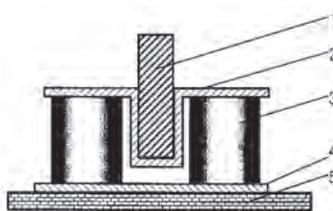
Конструктивная схема резинового виброизолятора обычного типа: 1–лапа станка; 2–S - образный кронштейн; 3–резиновый упругий элемент; 4–опорная поверхность; 5–межэтажное перекрытие.
